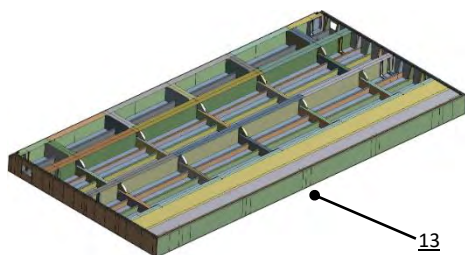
Вариант упрощённой конструкции крышки без интеркостельных связей, со сплошными взаимно перпендикулярными балками и замкнутым контуром поперечного сечения продольной балки у свободной кромки (вид снизу)
